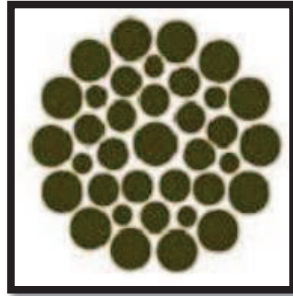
Sección transversal torón tipo Warrington-Seale 36 alambres.
